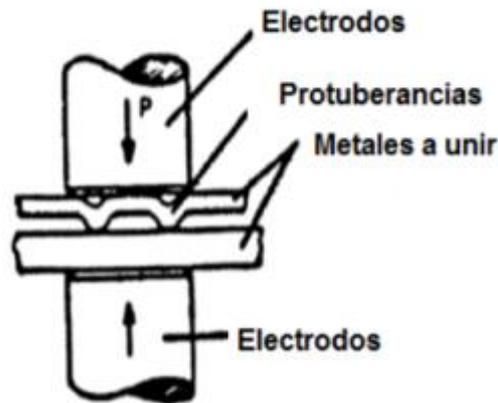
Esquema de soldadura por protuberancias. [7]
